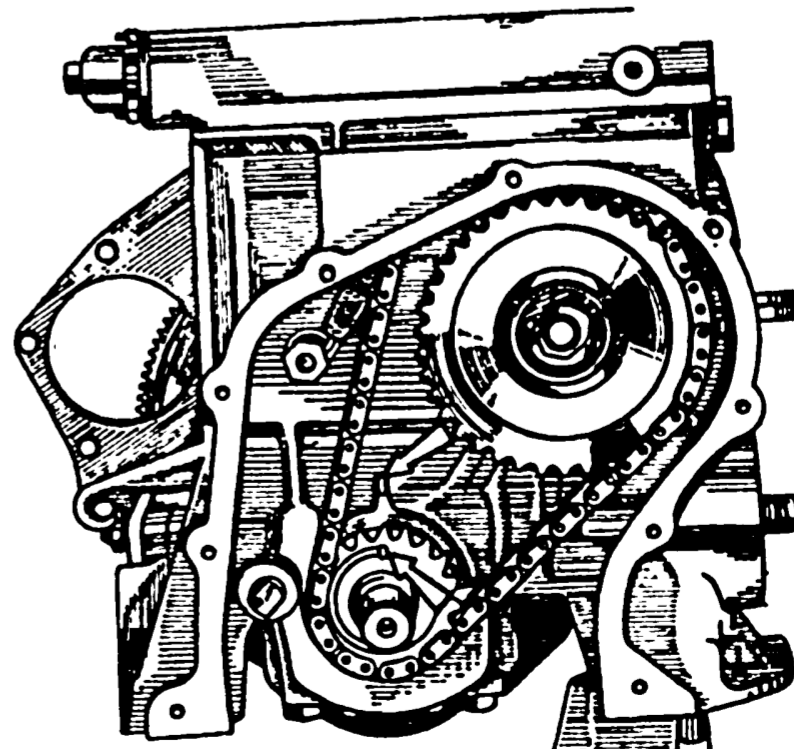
Проверка совпадения установочной метки на звездочке коленчатого вала с меткой на блоке цилиндров
